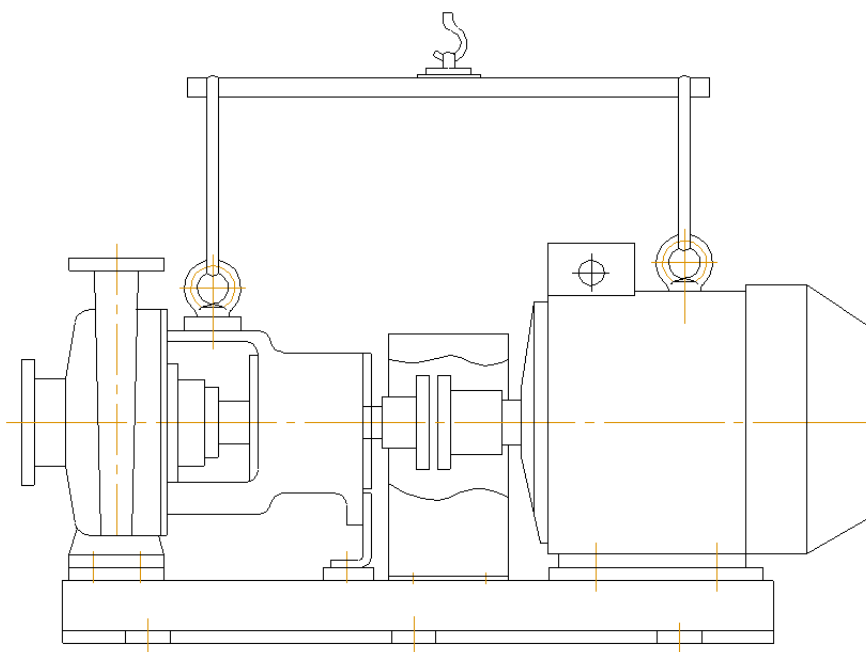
Строповка агрегатов типа «AX» и «AXO».
